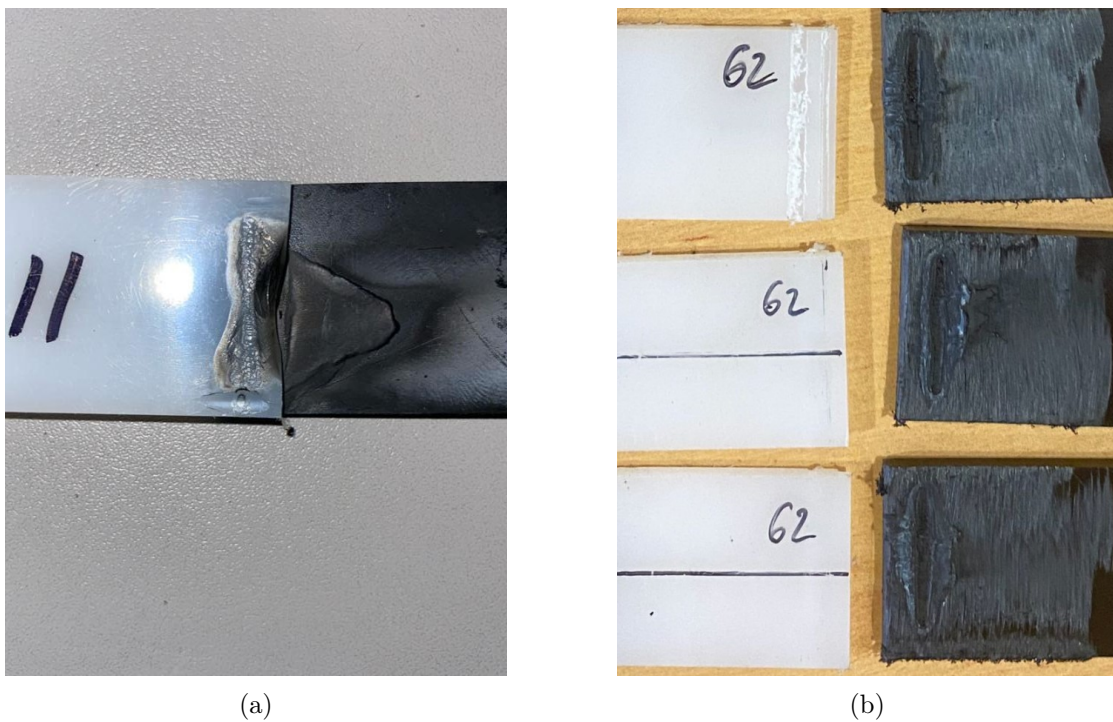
a) Aspecto da soldadura nas amostras iniciais (sinais de explosão de material e irregularidades); b) Aspecto da soldadura após otimização de parâmetros (soldadura uniforme e nítida).
